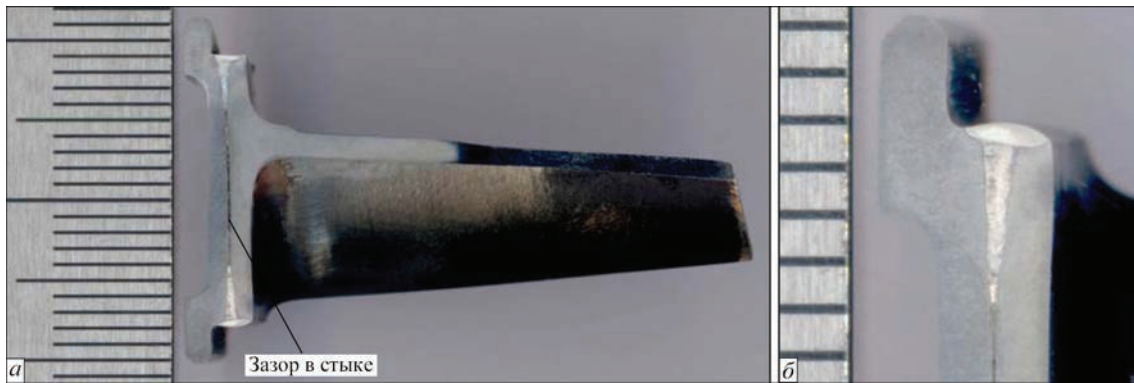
Макрошлиф поперечного сечения ЭЛ-соединения лопатки с полукольцом направляющего аппарата, полученного при зазоре в стыке до 0,1 мм (а) и область сечения, содержащая сам сварной шов (б)
